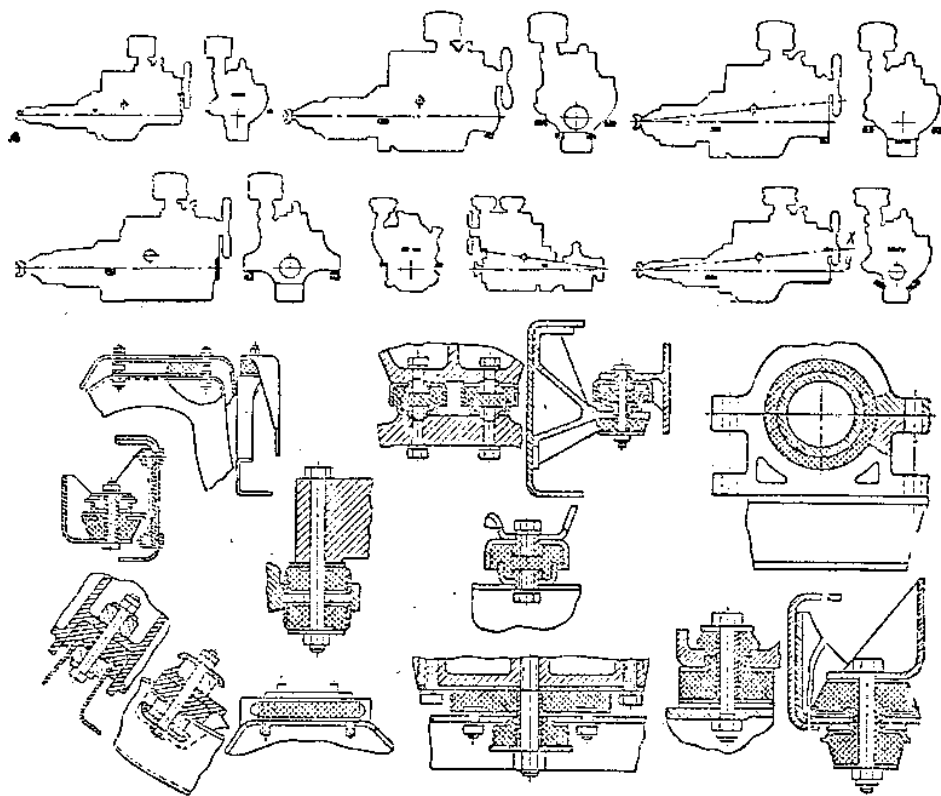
Схеми підвіски двигуна і конструкцій опор
